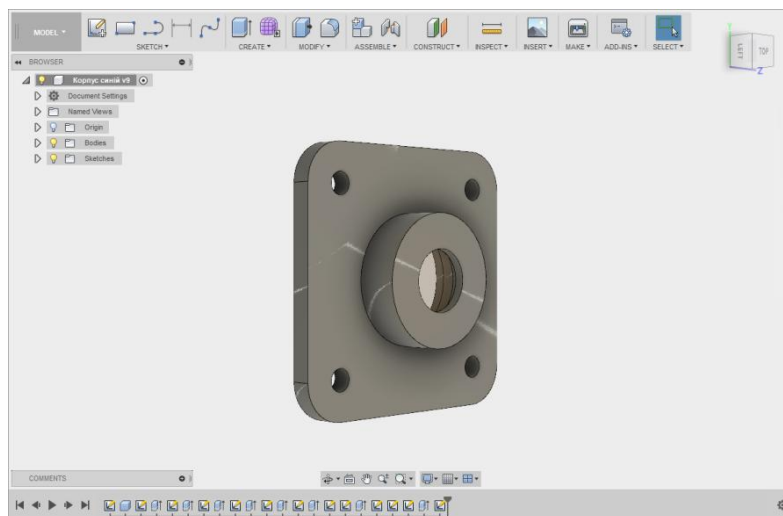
Графічна модель швидкозношуваної деталі (корпус підшипника)
